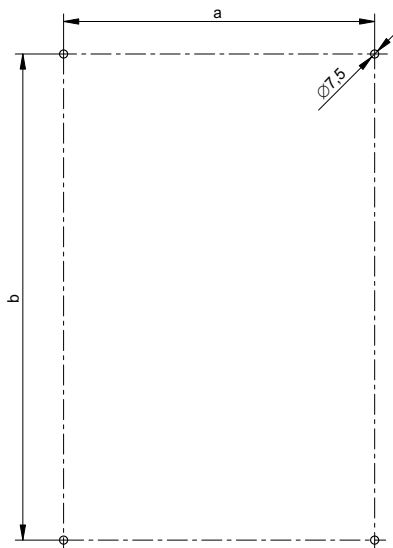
Габаритные размеры / Figure 1 – Overall dimensions
